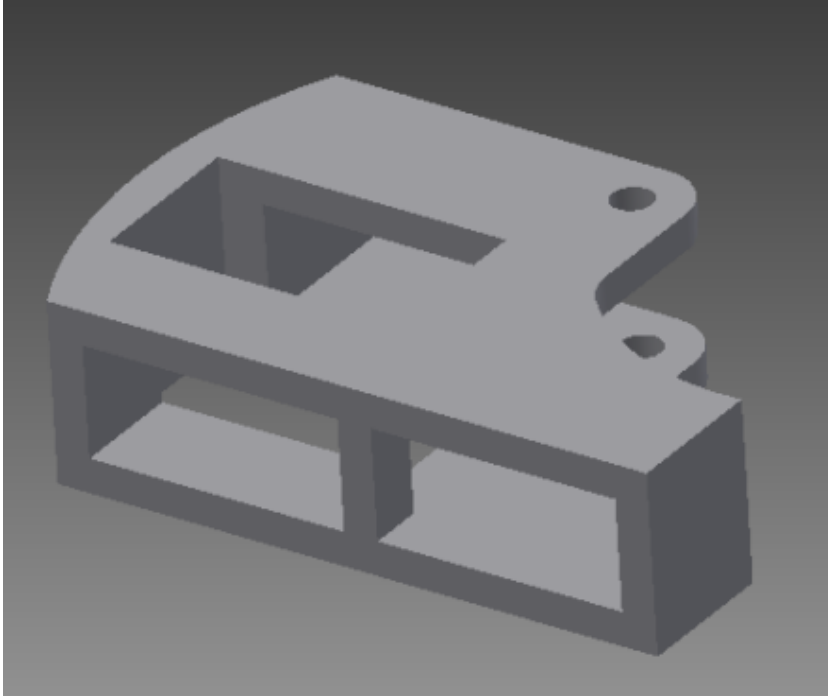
Δημιουργία οπής τοποθέτησης ήλου με την χρήση της εντολής hole
